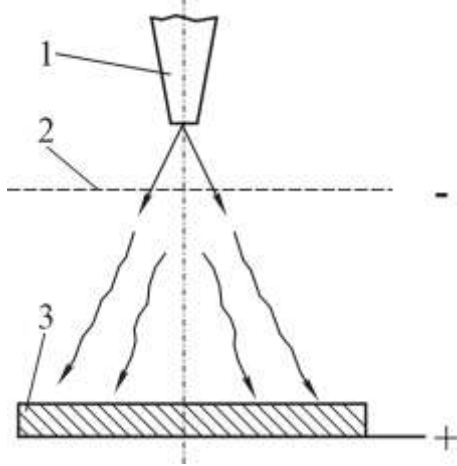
Схема нанесення на контрольовану поверхню пенетранта в електростатичному полі: 1 – сопло; 2 – металева сітка; 3 – деталь
